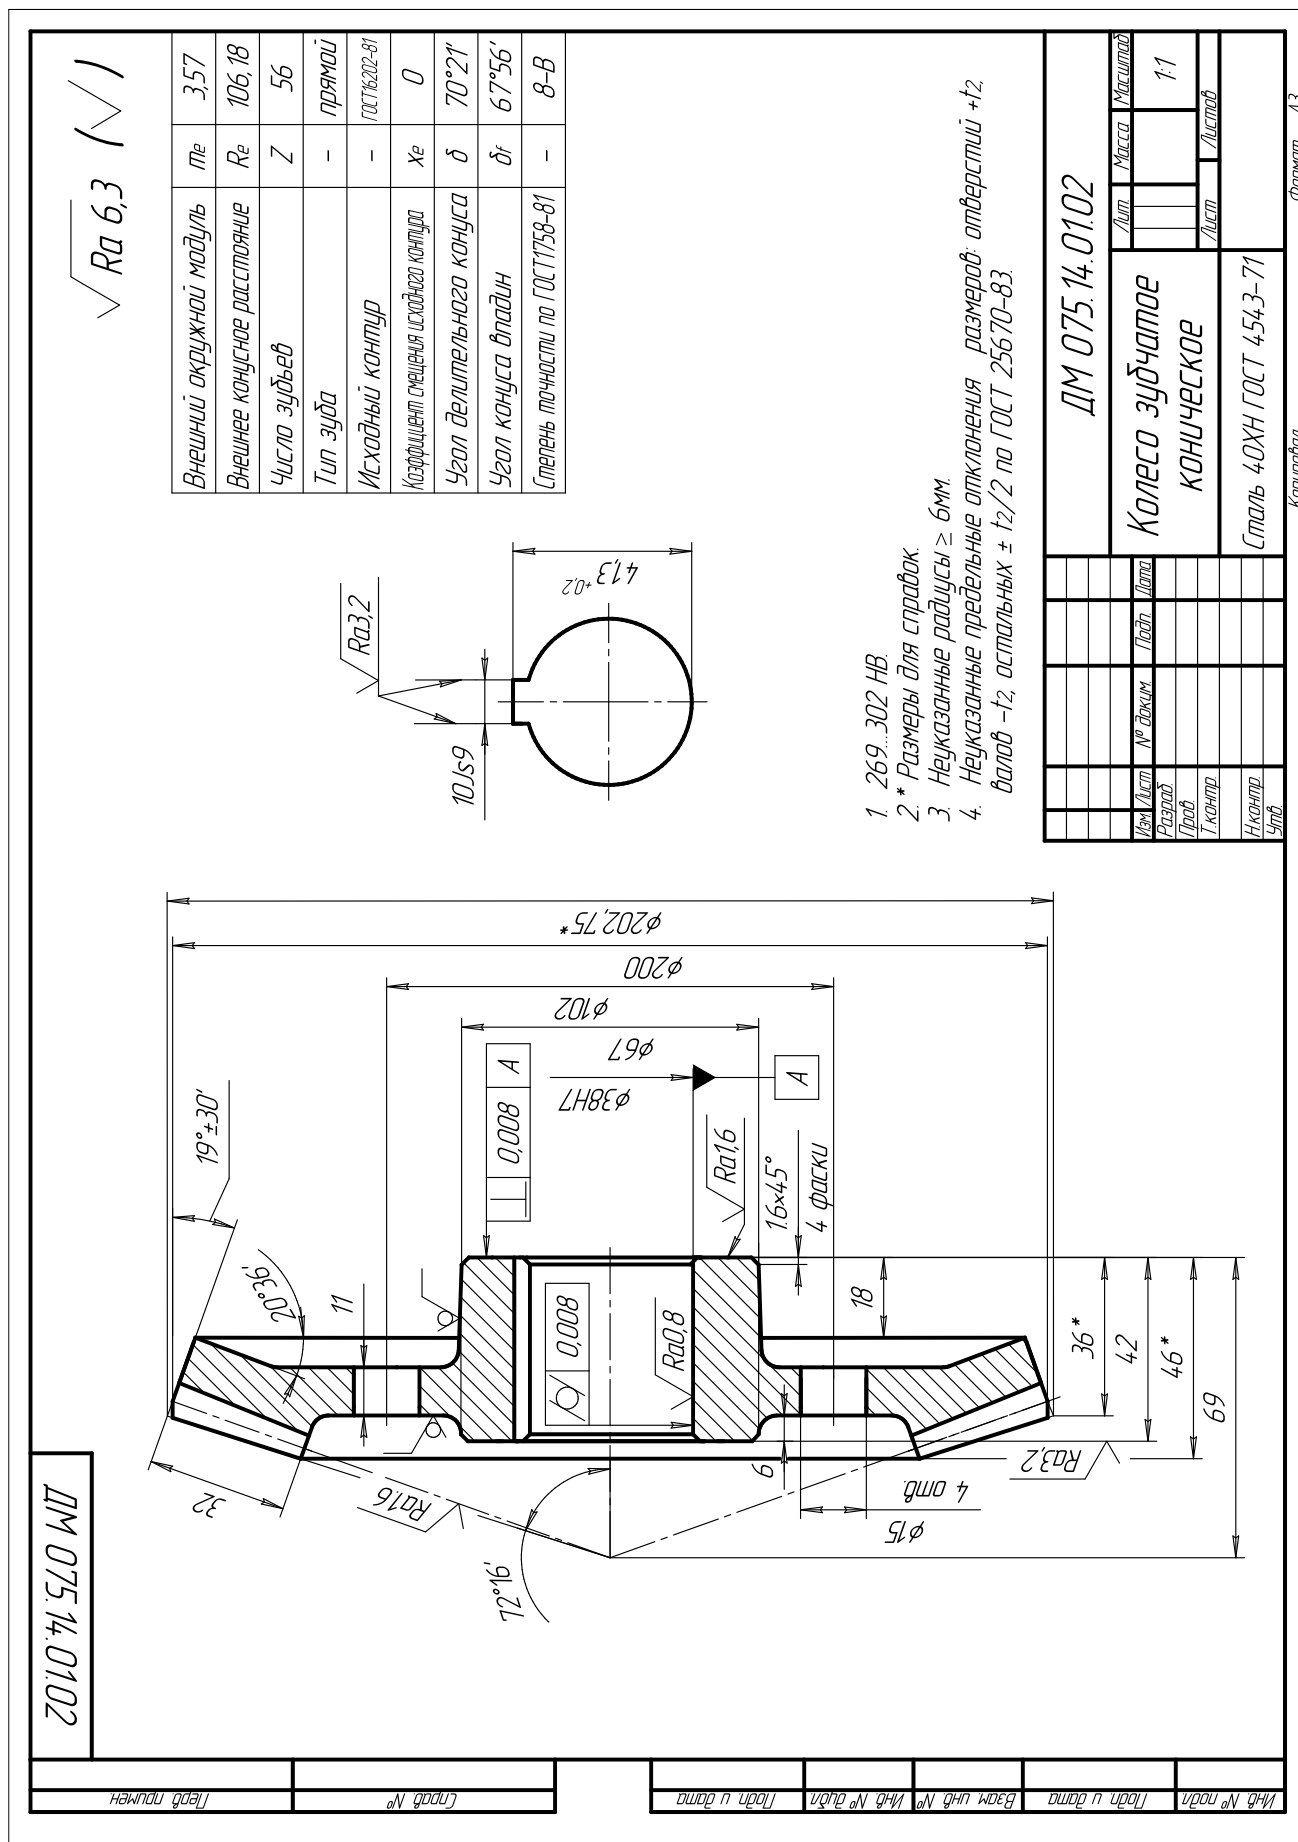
Пример оформления рабочего чертежа конического колеса
